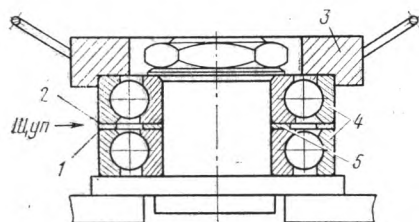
Приспособление для определения толщины колец при спаривании радиально-упорных подшипников:
